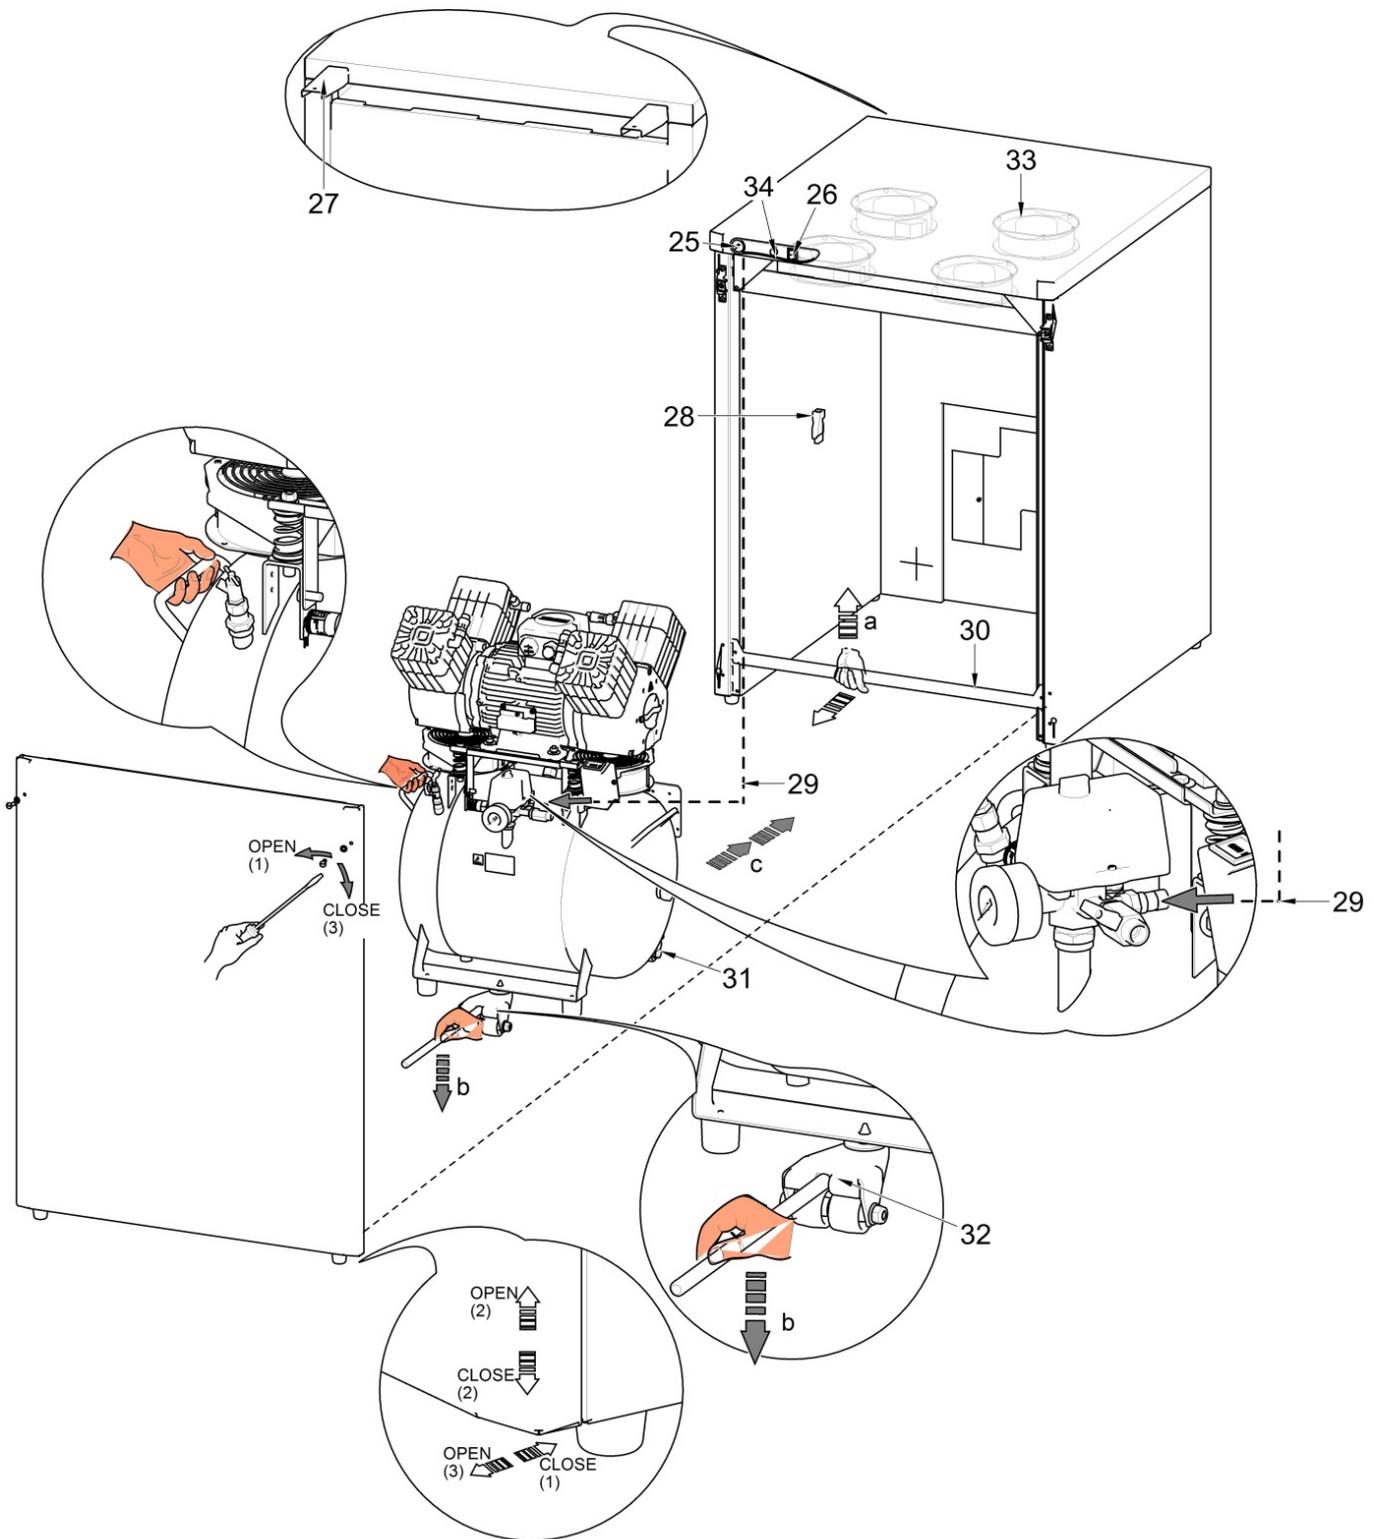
Kompresor s membránovou sušičkou (MD)
